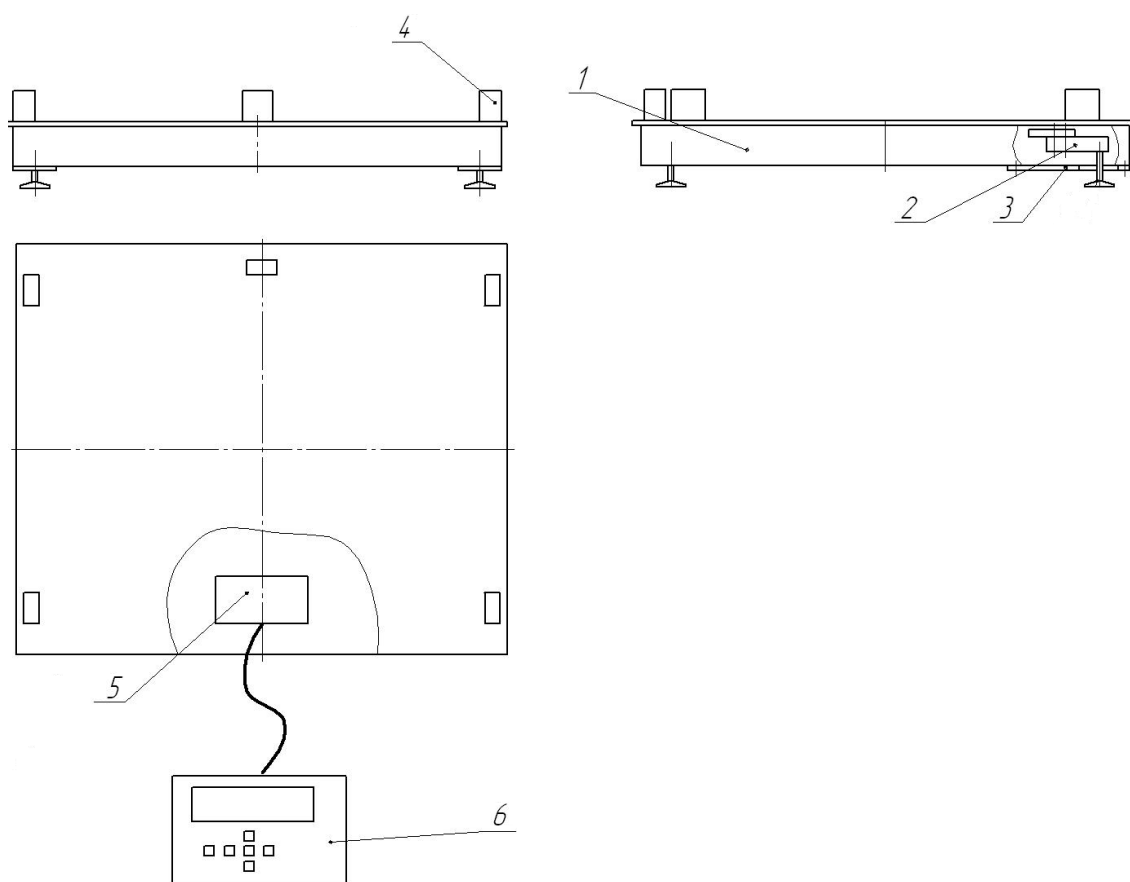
Общий вид весов (1 – платформа; 2 – весоизмерительный тензорезисторный датчик; 3 – крышка; 4 – элементы для установки перил; 5 – соединительная коробка; 6 – электронное весоизмерительное устройство)
